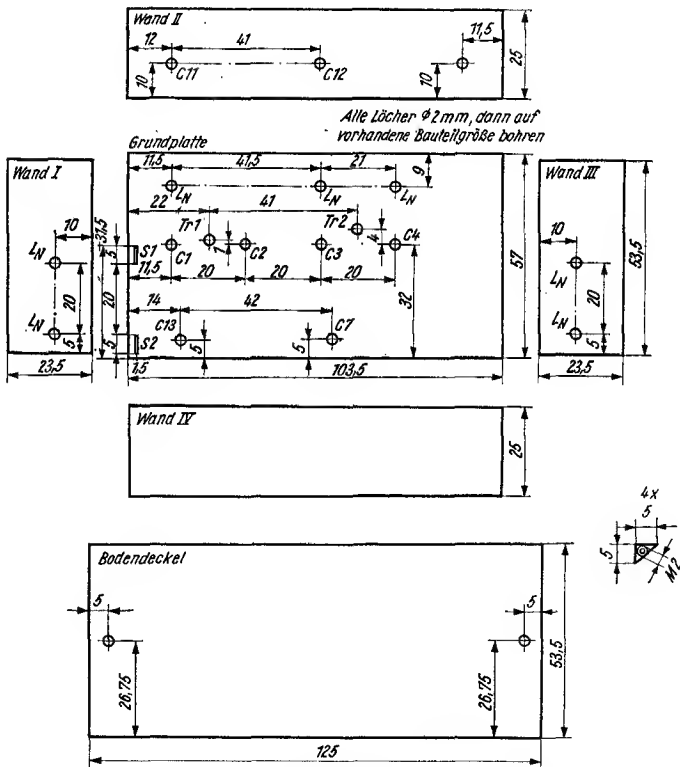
Bauteile des Chassis aus kupferkaschiertem Schichtpreßstoff
